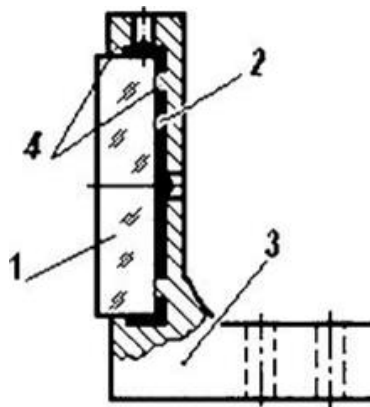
Кріплення дзеркала з установкою на опорні пояски
